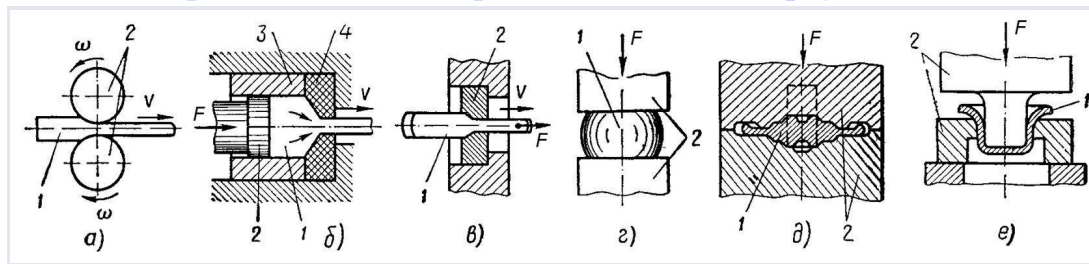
Види обробки металів пластичним деформуванням: а) - прокатка; б) - пресування; в) - волочіння; г) - кування; д) - об'ємне штампування; е) - листове штампування.
